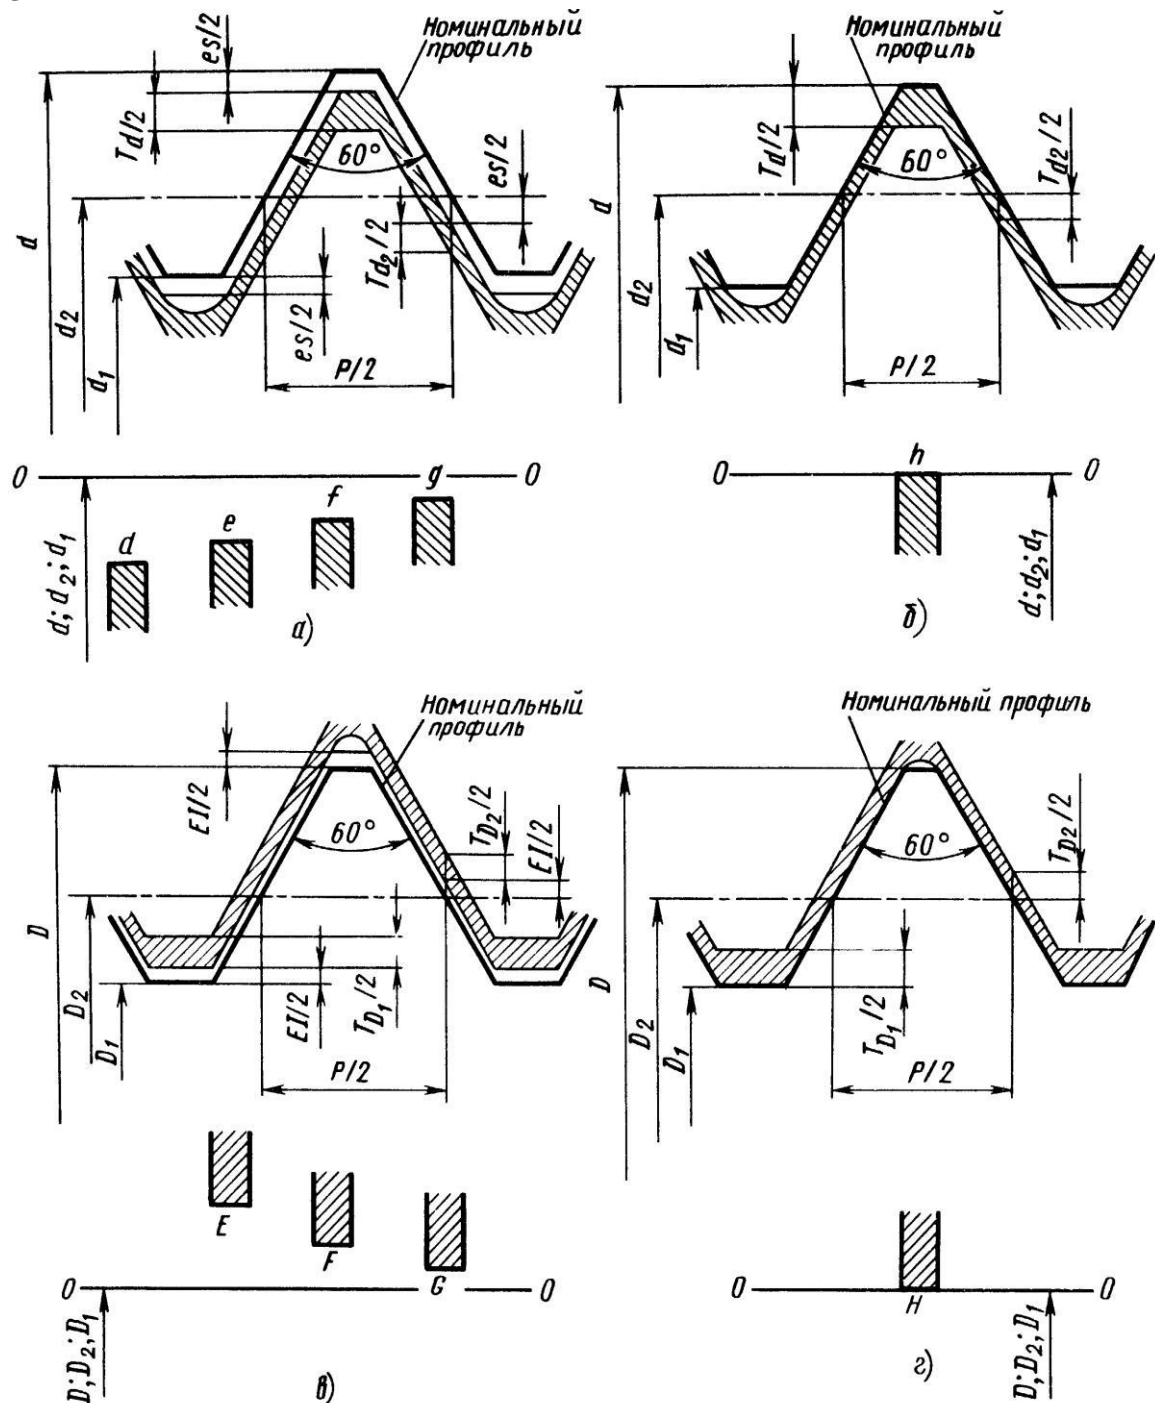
Схемы расположения полей допусков для посадок с зазором наружной (вверху) и внутренней (внизу) метрической резьбы с основными отклонениями d, e, f, g, (а); h (б); E, F, G, (в); H (г)
